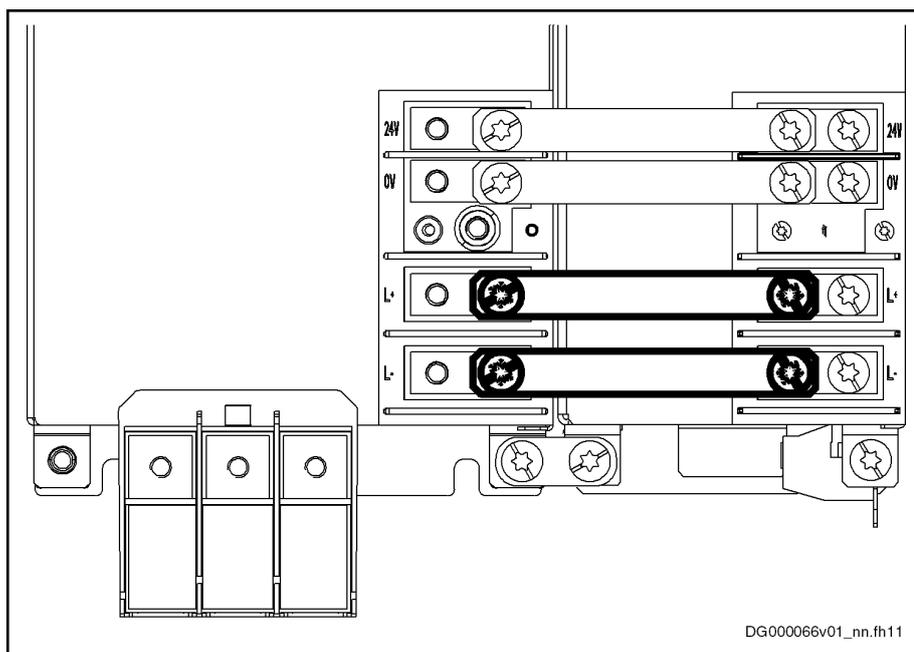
Collegamento del circuito intermedio con sbarre collettrici
